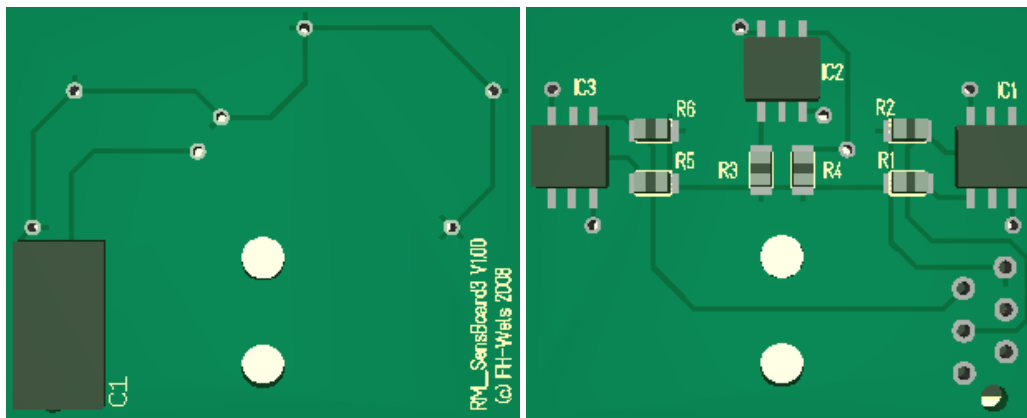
Linienboard 3Sensor - 3D-Ansicht - Top & Bottom
